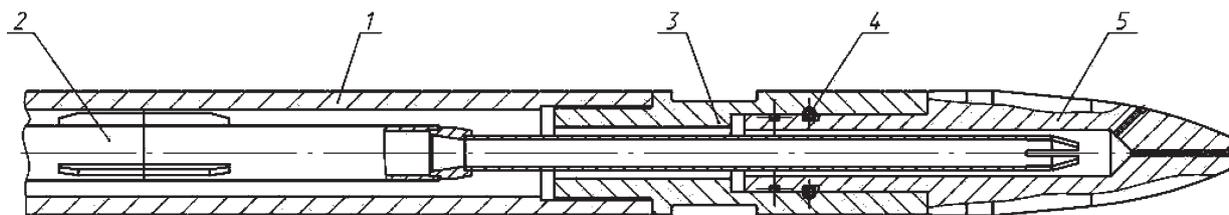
Новая конструкция прошивной оправки: 1 – корпус; 2 – коллектор; 3 – адаптер; 4 – штифт; 5 – оправка
